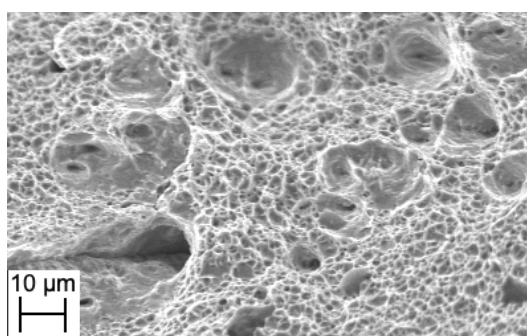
Superfície de ruptura do corpo de prova somente de metal base (Hardox 450) e sem soldagem.
